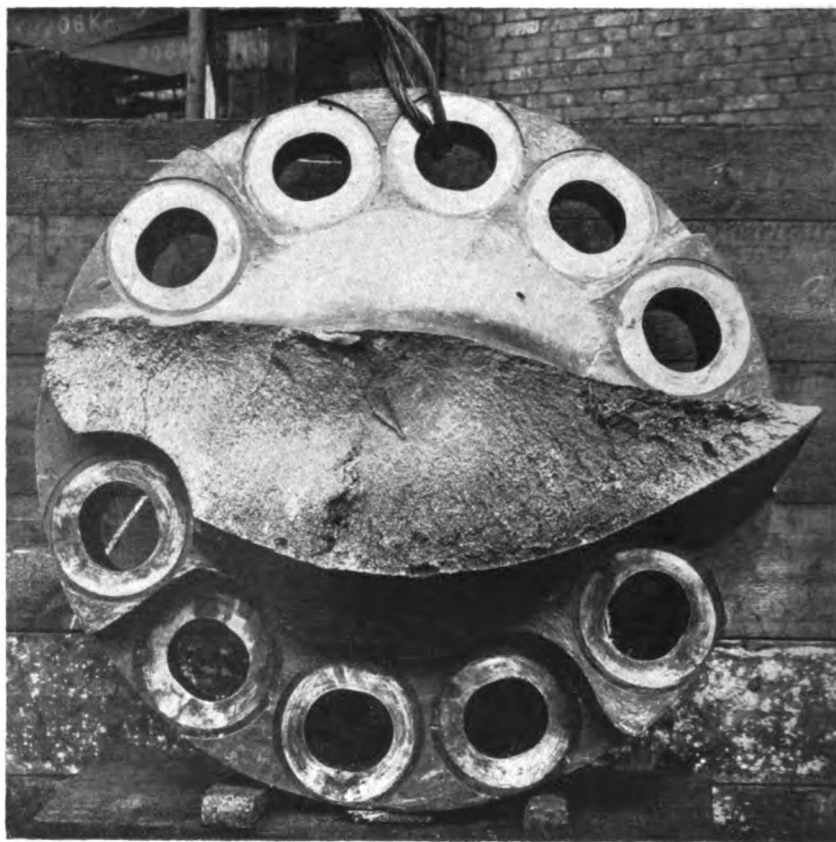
Bruch eines Propellerflügels bei einem Schnelldampfer, dessen Propellerflügeldurchmesser 7,3 m betrug
